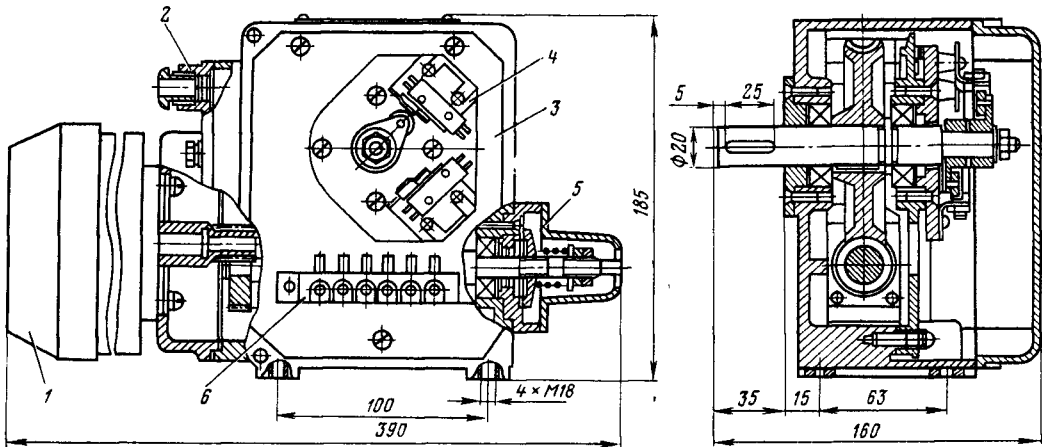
Общий вид, габаритные и присоединительные размеры механизмов ИМТМ-40/2,5-83:
